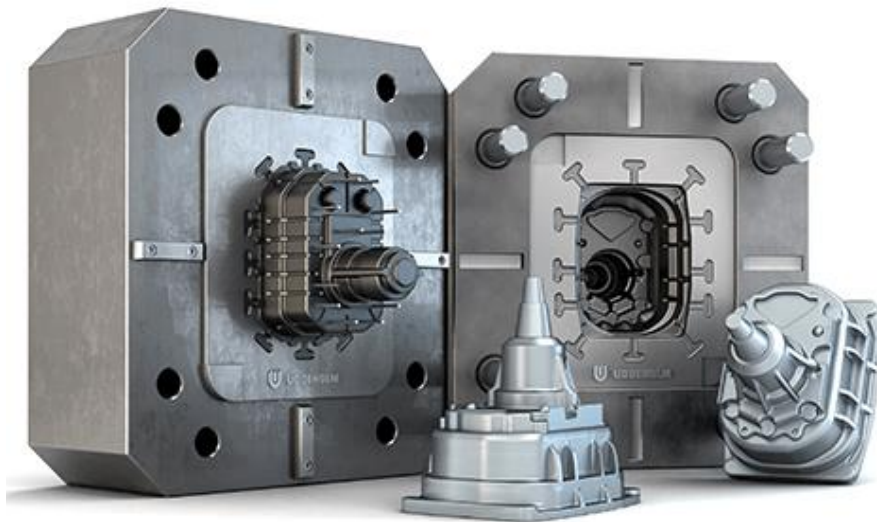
Ejemplo de moldes en acero para fundición inyectada de aluminio. Fuente: uddeholm.com
